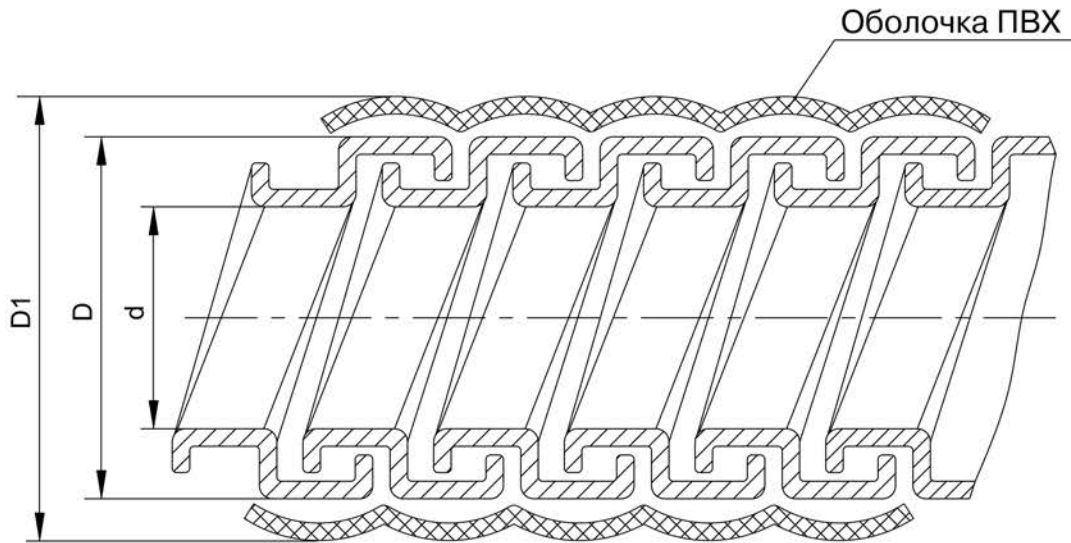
Металлорукав типа РЗ-ЦПнг и РЗ-ЦПнг-ХЛ с протяжкой
